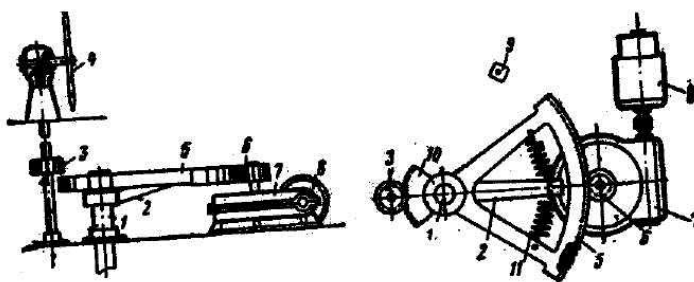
Электрический секторно-зубчатый привод. 1 – баллер; 2 – румпель; 3, 6 – шестерни; 4 – штурвал ручного привода; 5 – зубчатый сектор; 7 – червячный редуктор; 8 – электродвигатель; 9 – ограничитель; 10 – зубчатый сектор ручного привода
